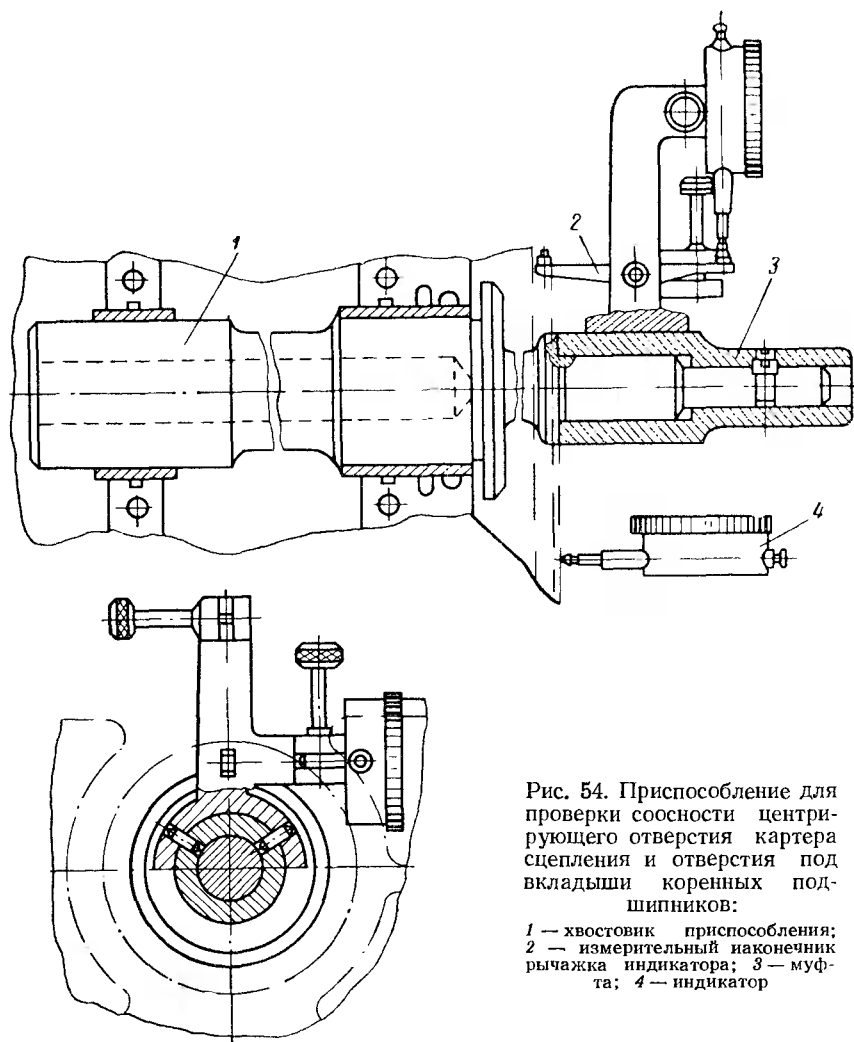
Приспособление для проверки соосности центрирующего отверстия картера сцепления и отверстия под вкладыши коренных подшипников:
